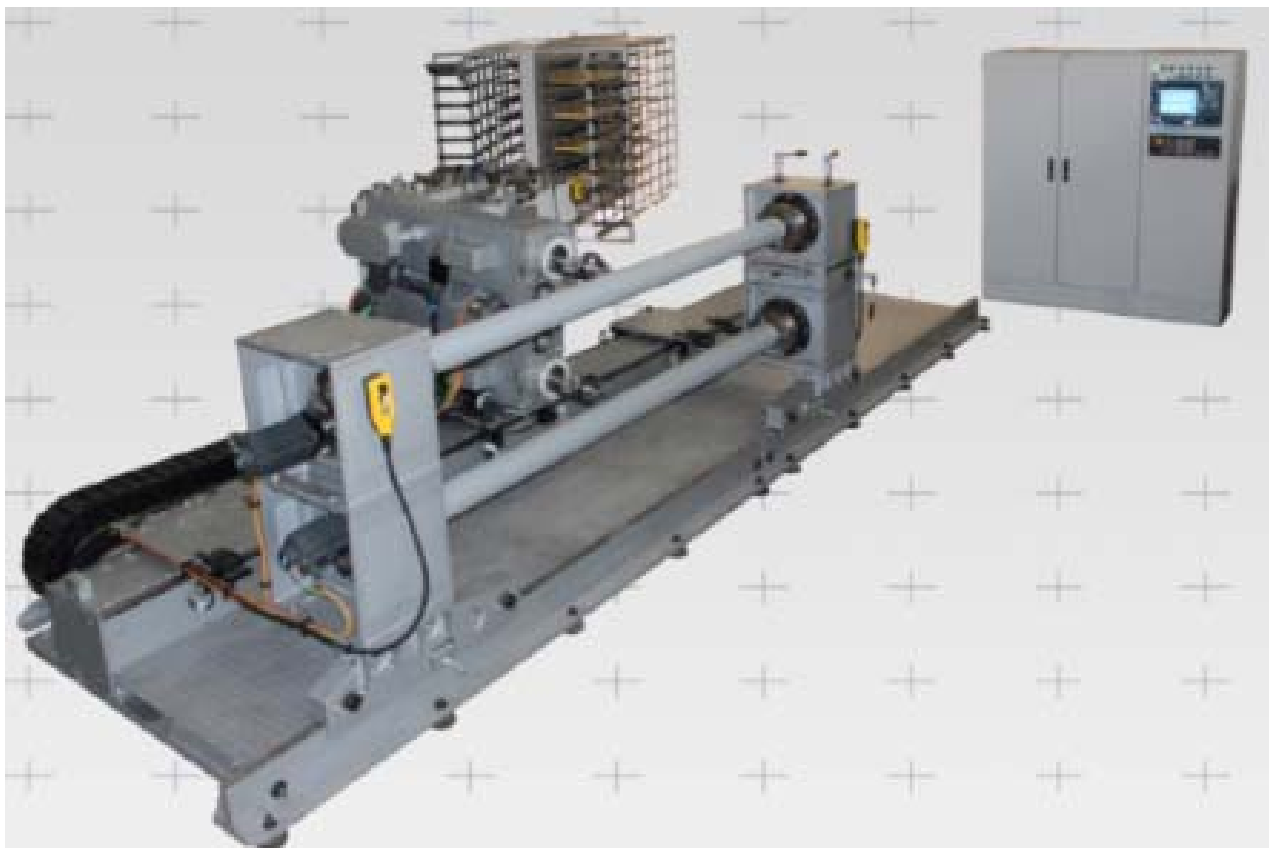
Общий вид двухшпindelного намоточного станка с ЧПУ
